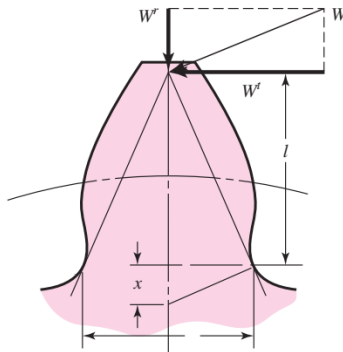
Perfil de diente de engranaje con la fuerza aplicada.
